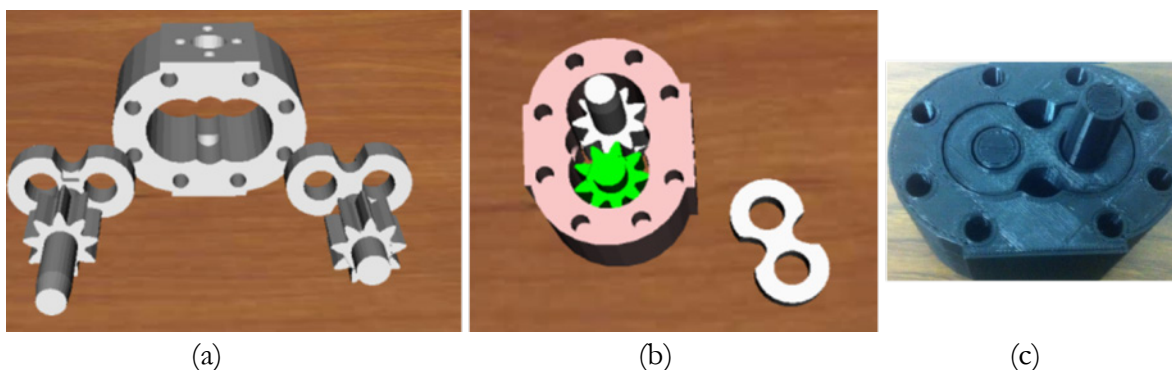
Caso de ensamble de bomba de aceite de engranes: (a) partes desensambladas, (b) proceso de ensamble, (c) prototipo real.
